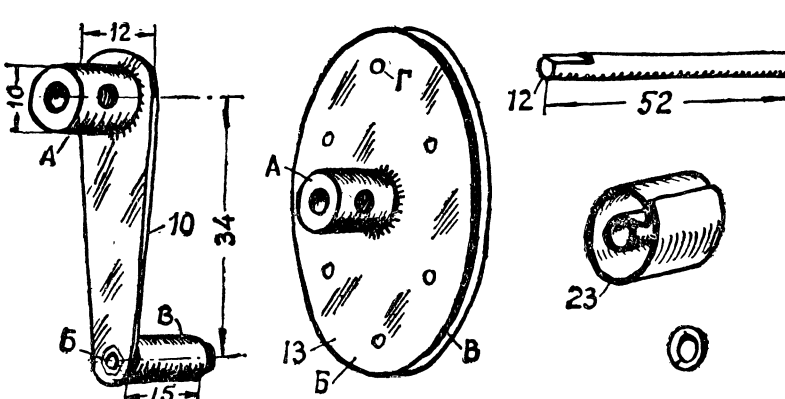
Детали привода: 10 — ручка; 12 — ось; 13 — ведущий шкив; 23 — приемная бобина
